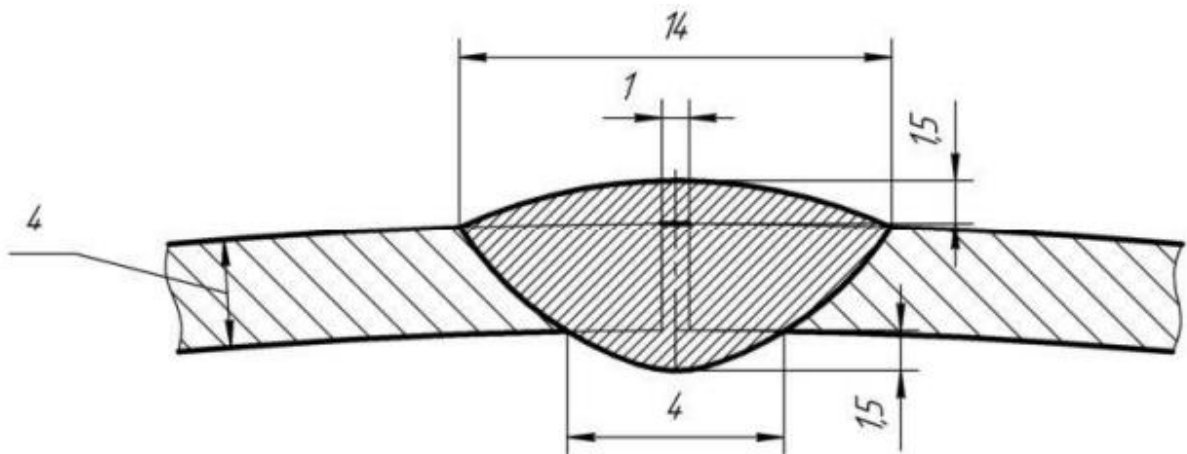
Схема зварного шва для автоматичного зварювання під шаром флюсу
